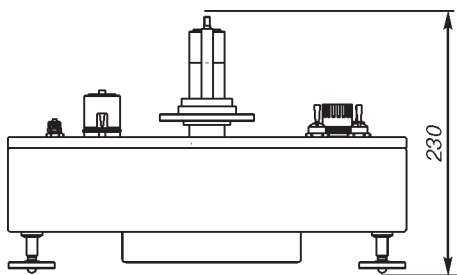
Калибратор давления пневматический 505 Воздух-I.
